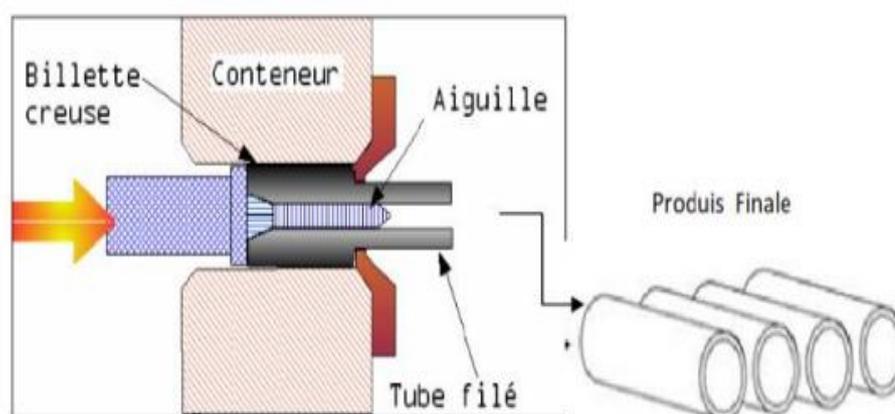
Fabrication de pipeline sans soudure [7].
